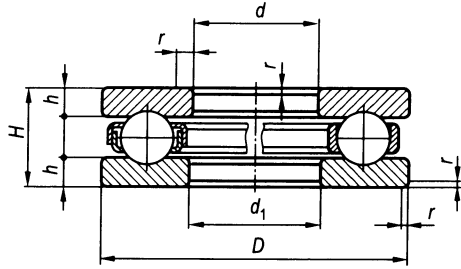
Подшипник шариковый упорный одинарный
